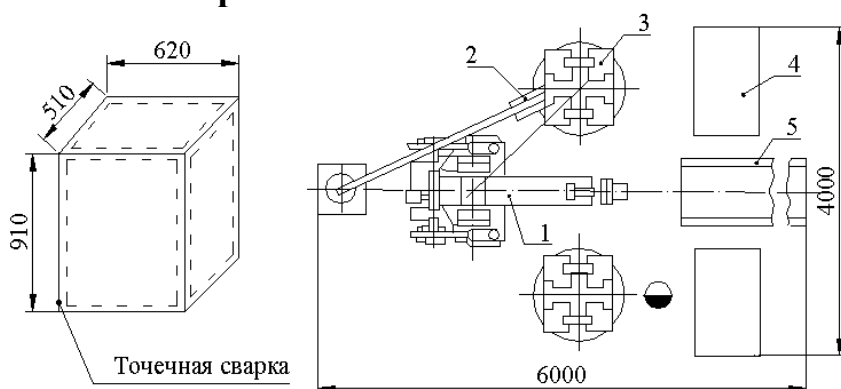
1 - ПР мод. PR - 32 напольного типа; 2 - подвесное устройство для точечной сварки мод. КРН 80.21.125; 3 - поворотный - позиционирующий стол (2 шт.); 4 - стол - спутник (2 шт.); 5 - отводящий конвейер тактового типа.
